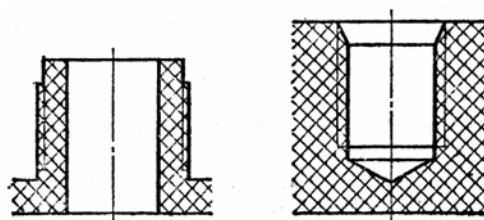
Конструкция наружной и внутренней формовой резьбы
